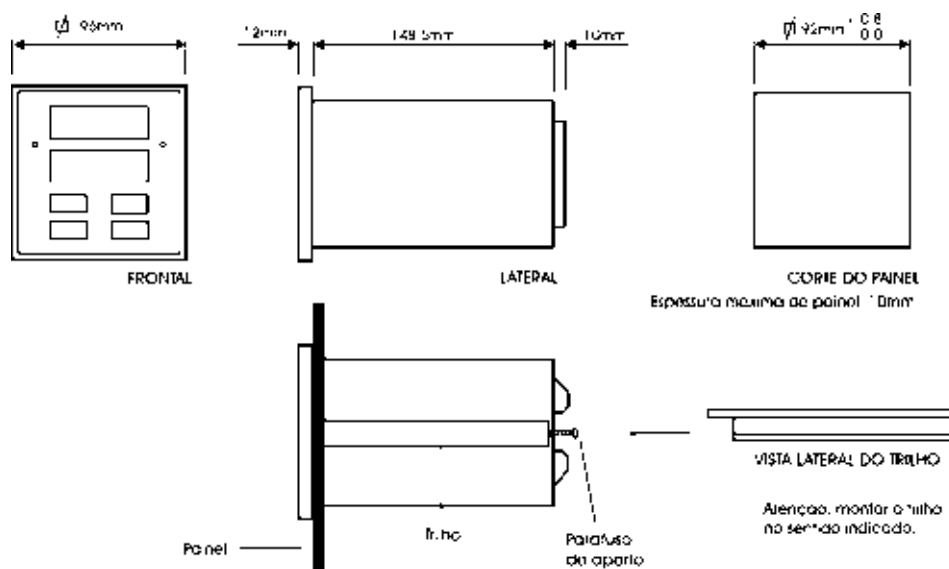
Desenho dimensional, corte e vista lateral da montagem no painel do controlador DCY-2060-LC.
